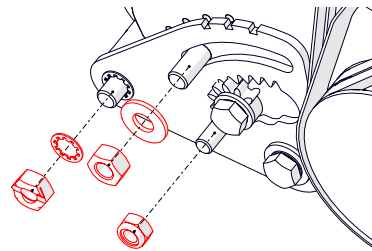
A – 3 Befestigungen wie abgebildet entfernen.
